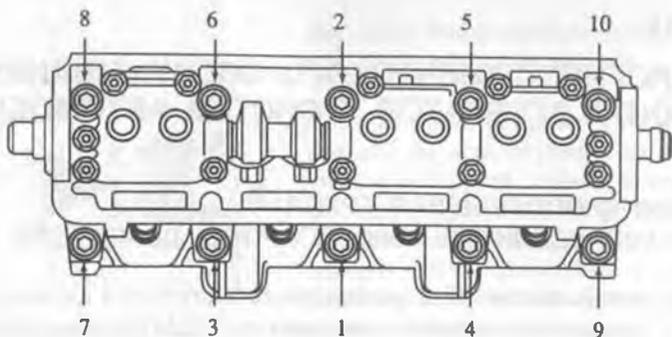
Порядок затягивания болтов крепления головки цилиндров
